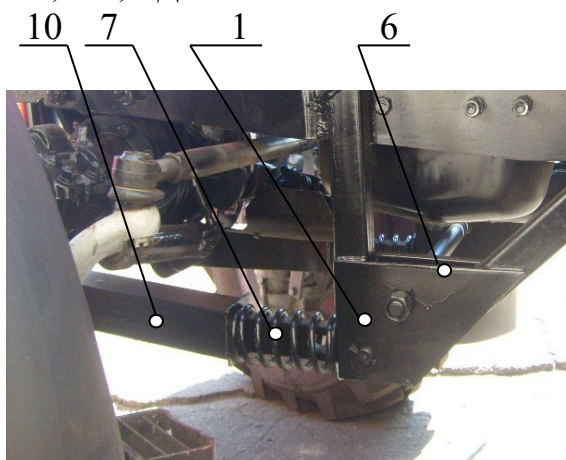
Сборка Подрамника, Вала распорного, Рамы.
